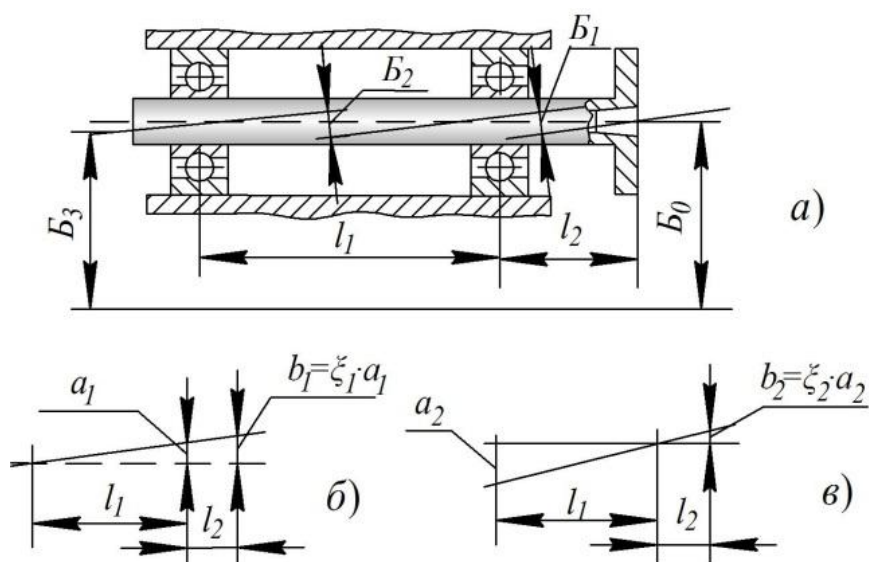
Вал, смонтированный в корпусе на двух подшипниках качения
